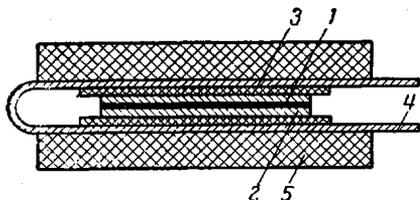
Приспособление для контактного нагревания соединяемого образца из стали и фторопласта:
